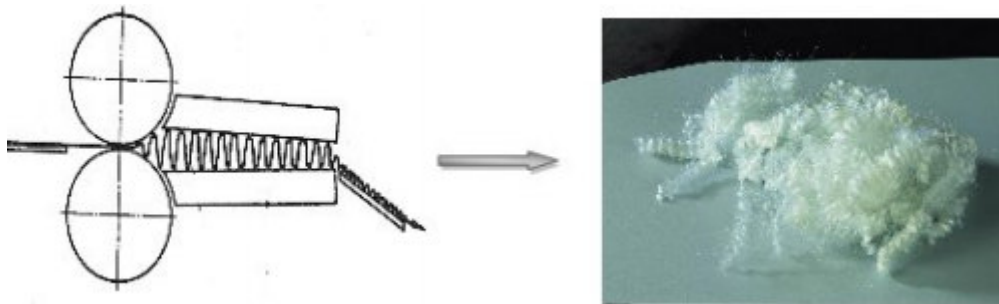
dispositif de machine de frisage de fibre (Crimper).
